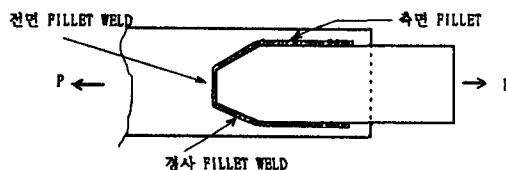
c(2) FILLET WELD의 종류(용접선과 힘 방향)
